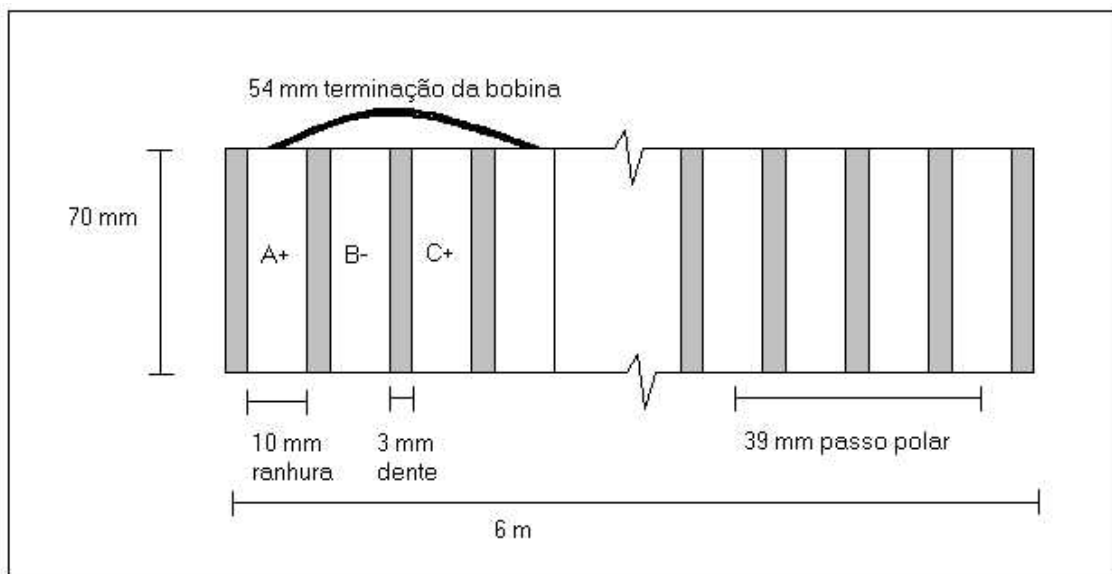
Enrolamento de Armadura, Vista Superior
